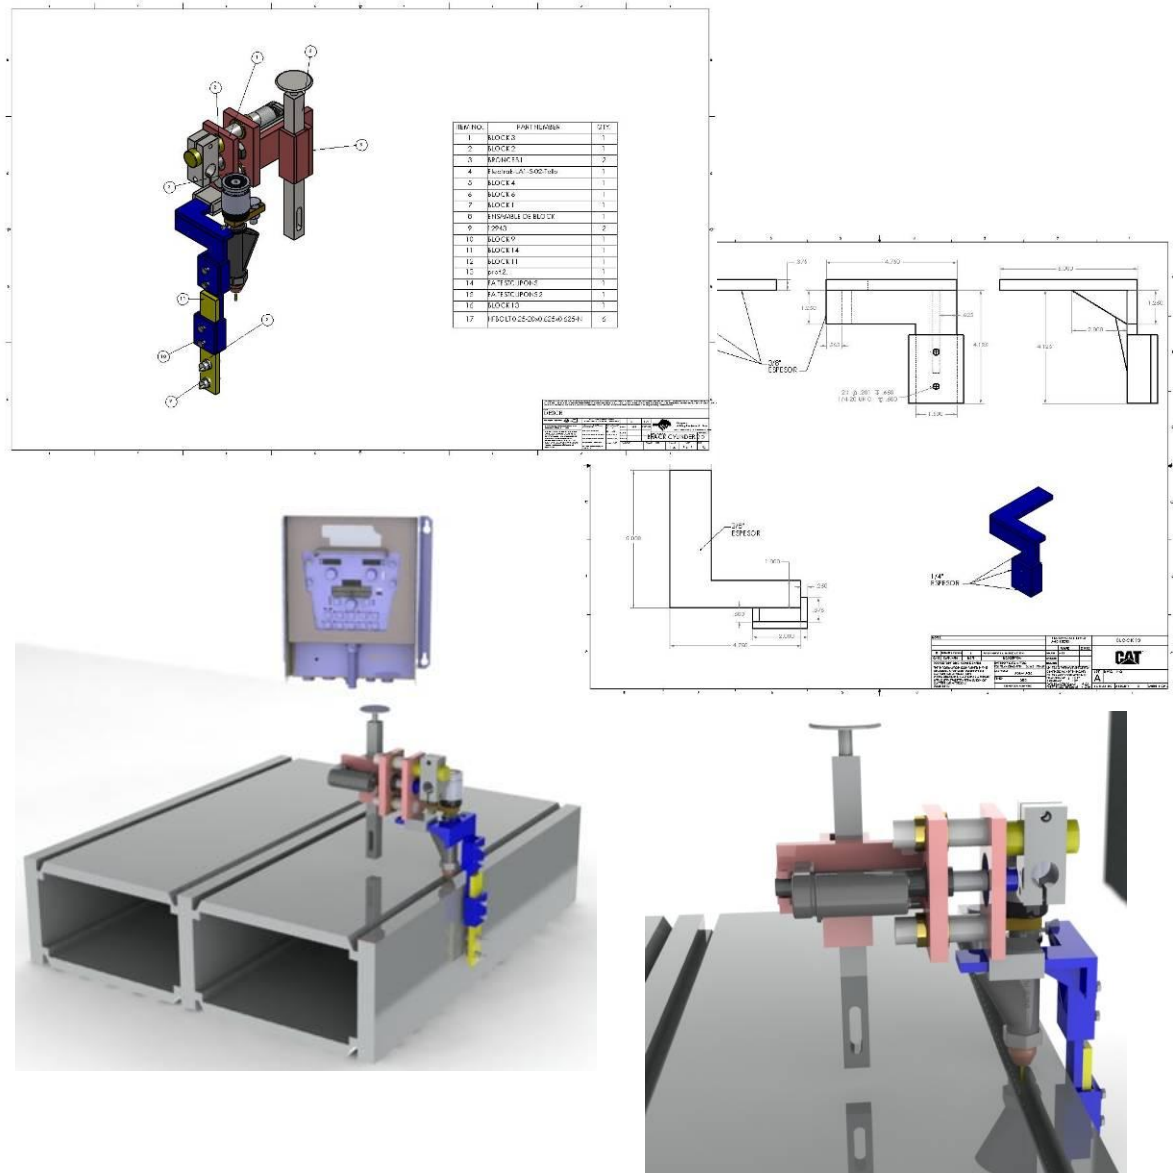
Diseño de dispositivo automático para seguimiento de junta.
